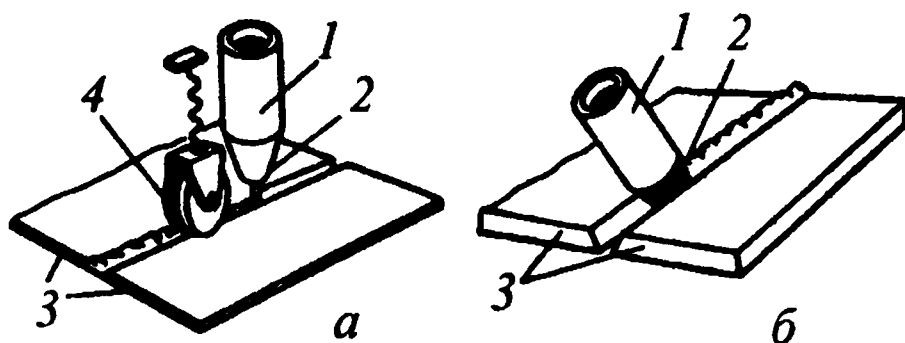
Схема бесконтактной (а) и контактной (б) экструзионной сварки расплавом: 1 — экструдер; 2 — мундштук экструдера, 3 — свариваемые детали; 4 — прокатывающий ролик
